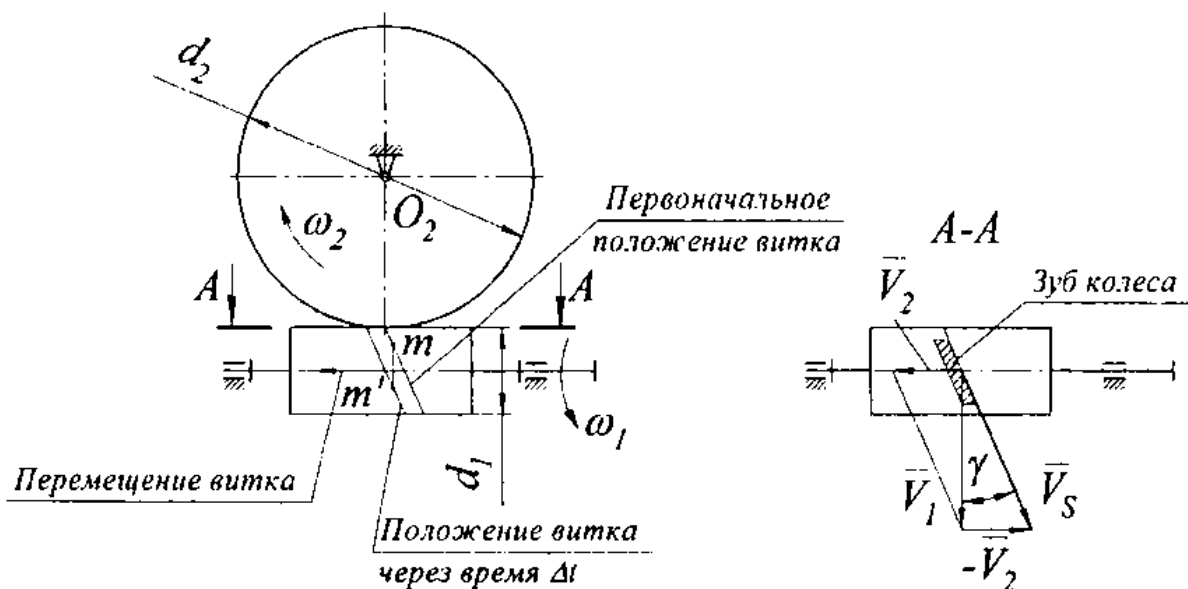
Кинематика червячной передачи с цилиндрическим червяком
